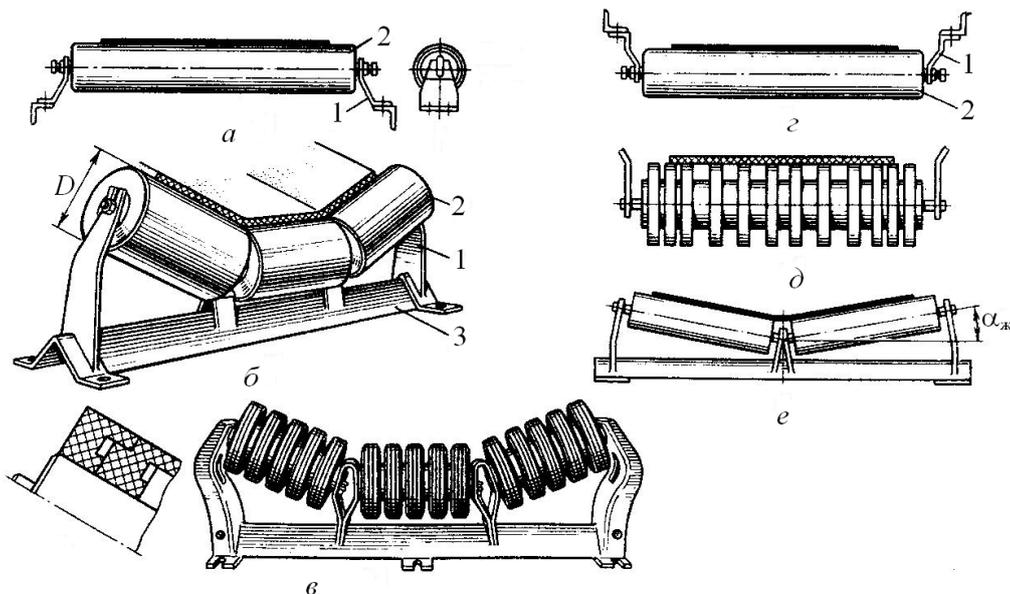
Роликоопоры ленточного конвейера:
